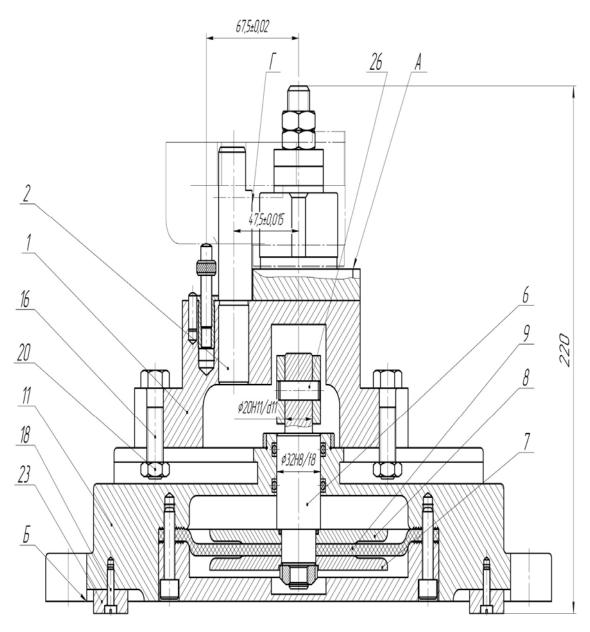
Сборочный чертеж приспособления для обработки детали «Корпус» (см. также с. 161)
